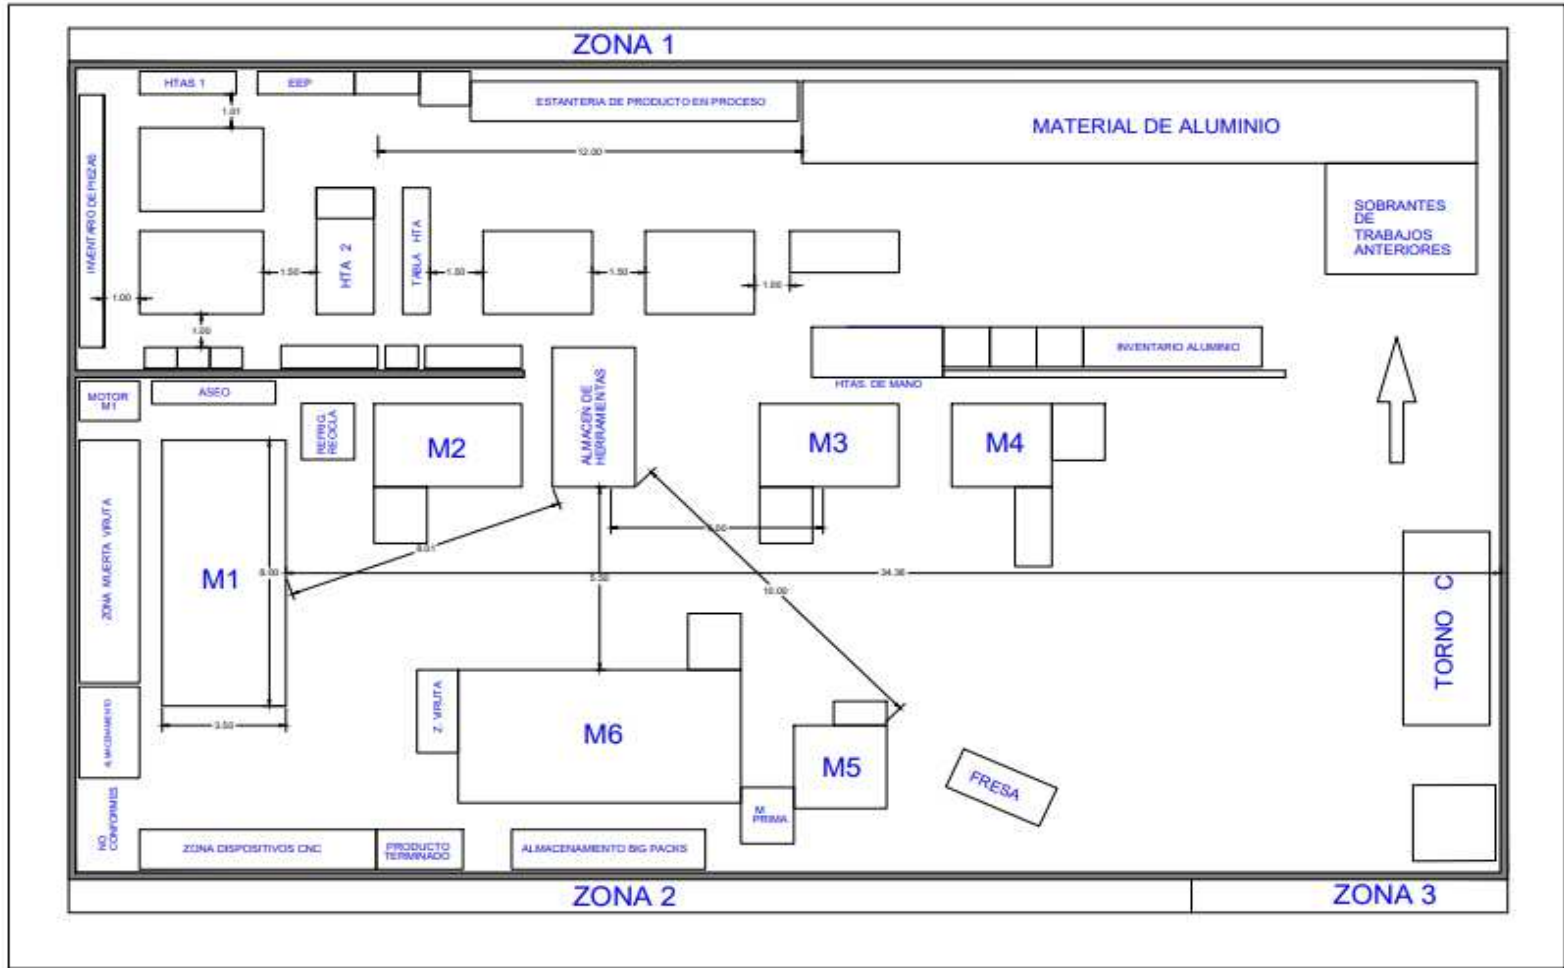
Layout. Autoría propia. Elaborado en AutoCAD.
